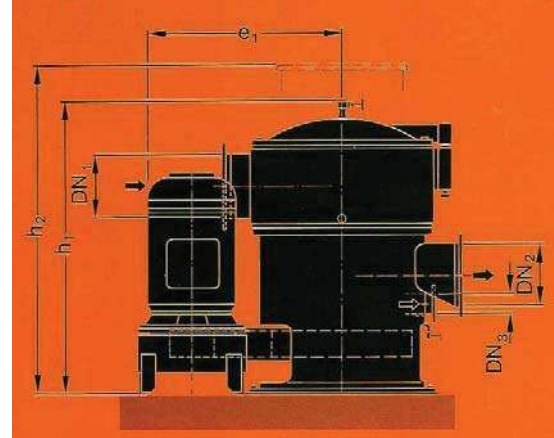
Dimensiones del fraccionador tamaño 100 y 200.
